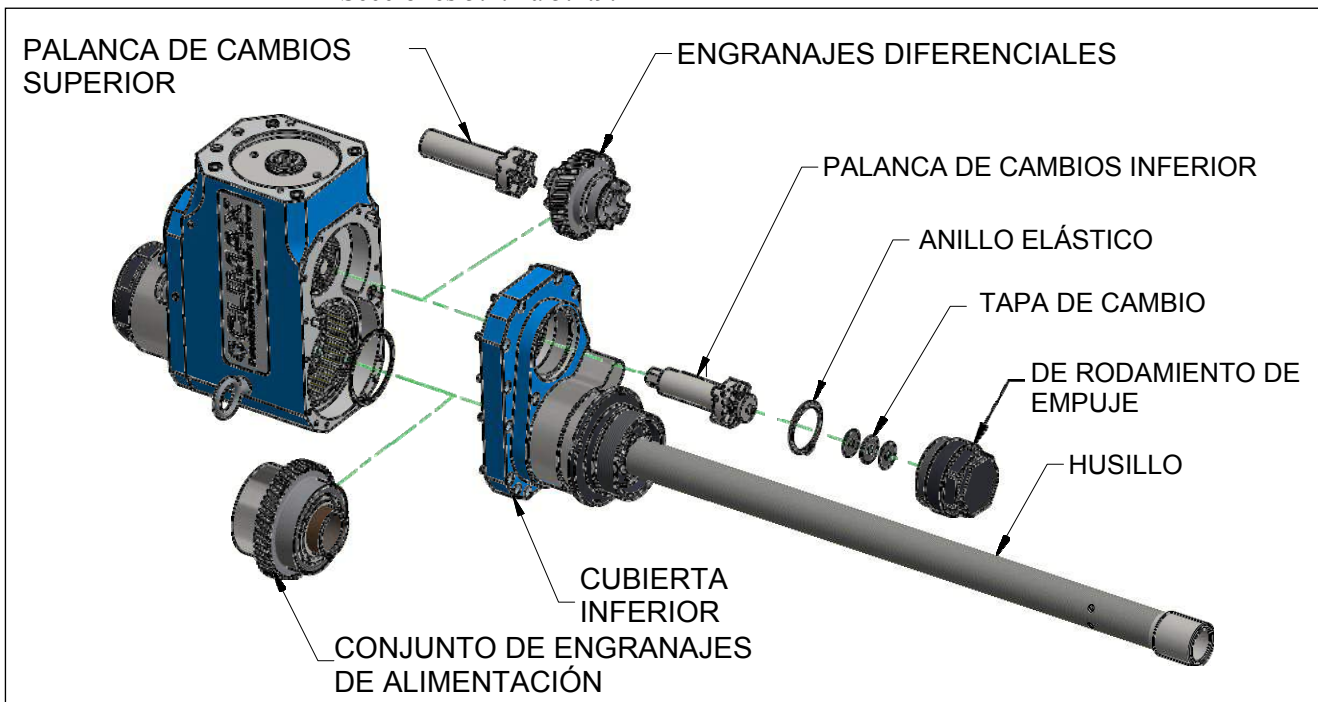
CONJUNTO DE CAJA DE CAMBIOS
